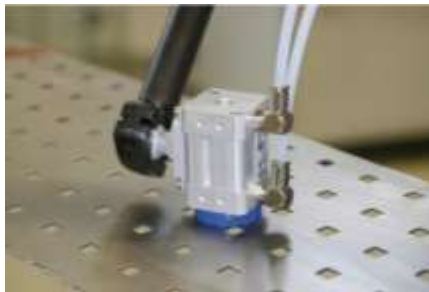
Gripper adhesivo, Fuente: TRAPO AG
